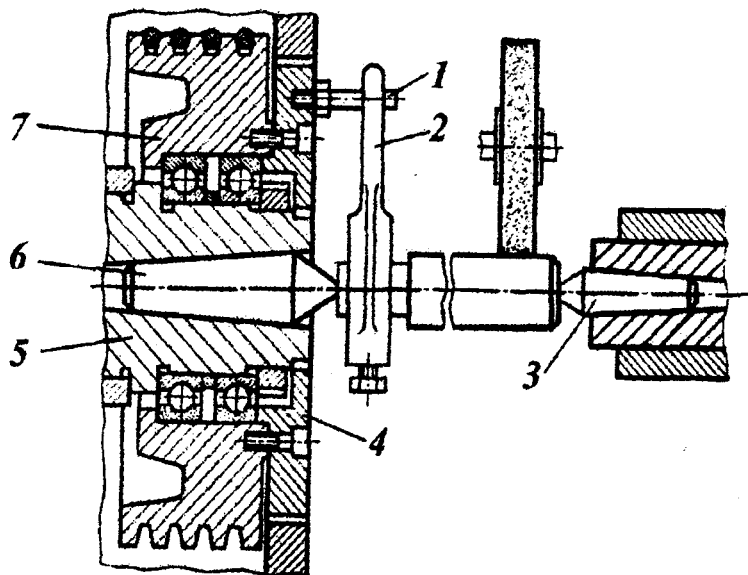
Схема установки шлифуемой заготовки в упорных центрах:
